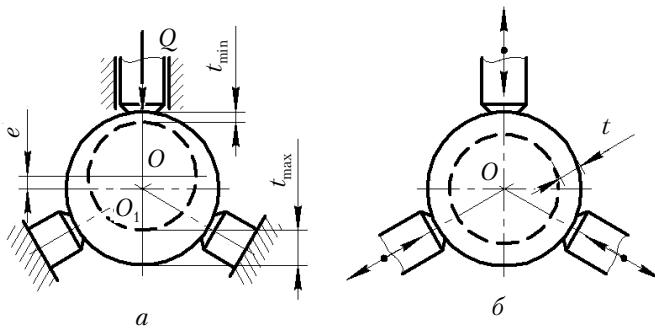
Варианты установки по цилиндрической поверхности при обтачивании на детали цилиндрической шейки:
